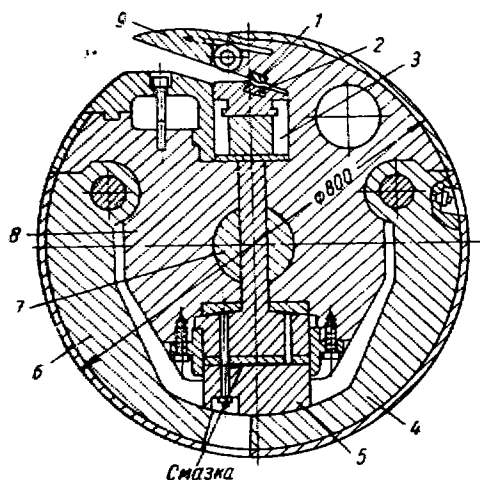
Барабан моталки непрерывного четырехклетового стана 2500 конструкции ВНИИМЕТМАШ
